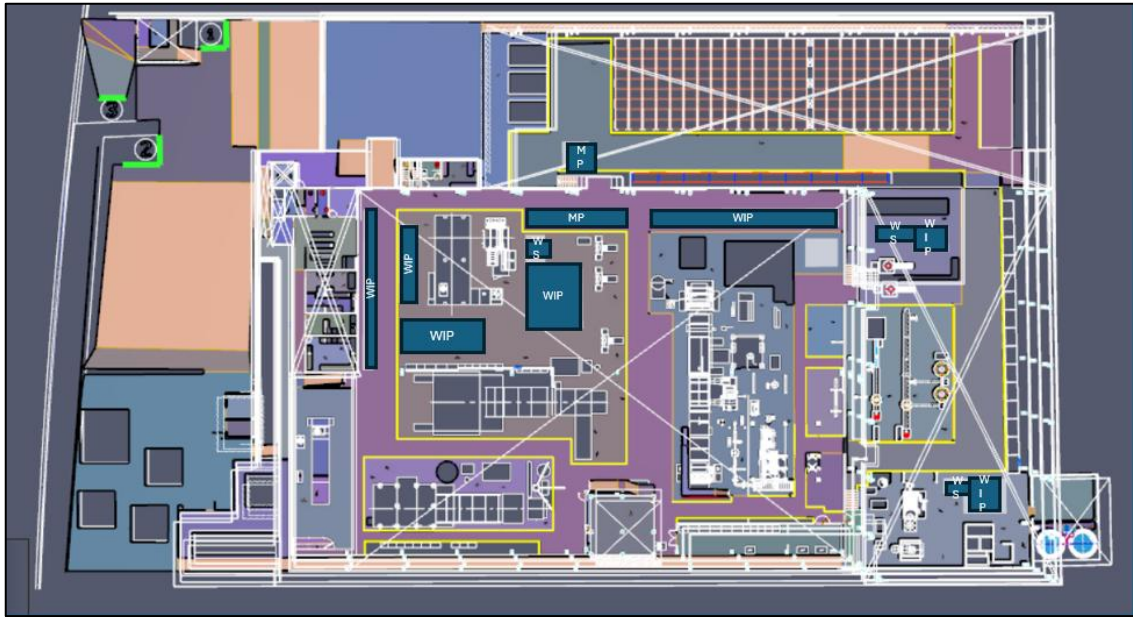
Modelo Ajustado para o Layout 2024 - Cenário 10
